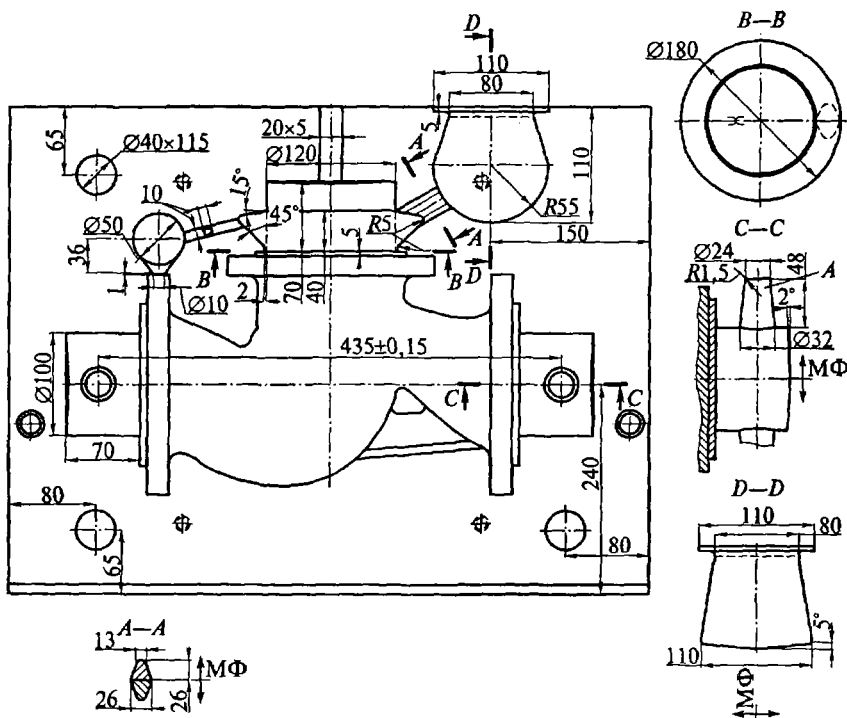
Чертеж модельного комплекта плиты для отливки арматуры, изготовляемой из серого чугуна на АФЛ типа «DISA»:
